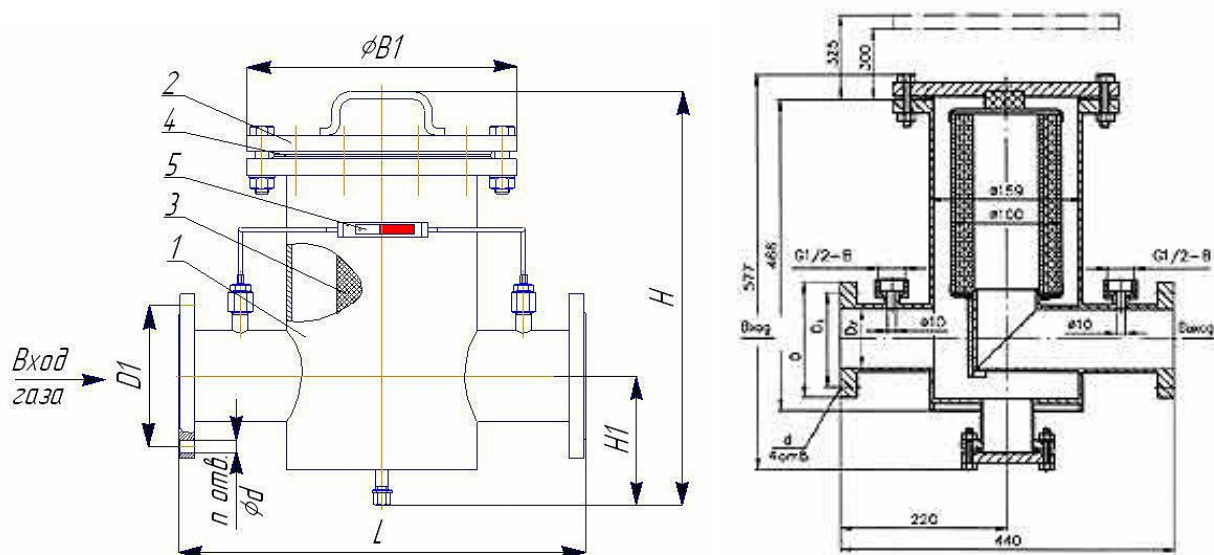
Фильтр газовый ФГ: 1 – корпус; 2 – отбойный лист; 3 – кассета; 4 – перфорированный лист; 5 – фильтрующий элемент; 6 – крышка; 7 – штуцеры; 8 – фланец
